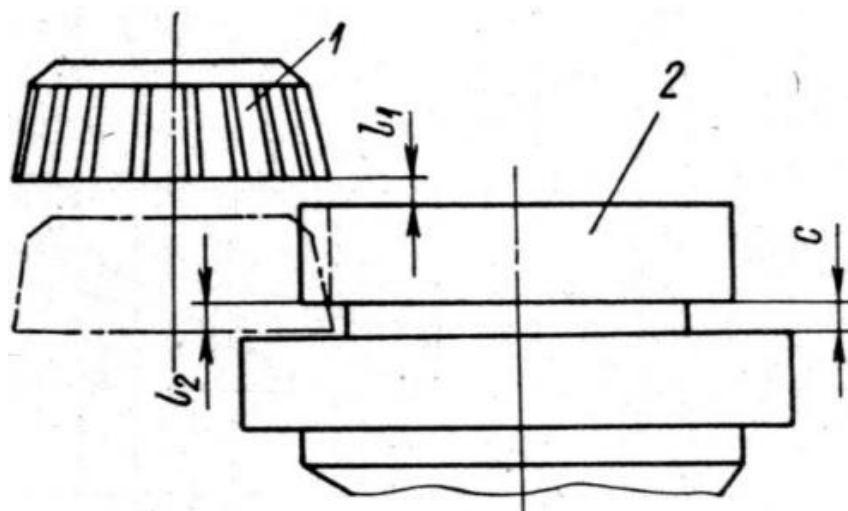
Эскиз перебегов долбяка при нарезании шестерни ступенчатого блока: 1 – долбяк; 2 – заготовка; с – ширина канавки.
